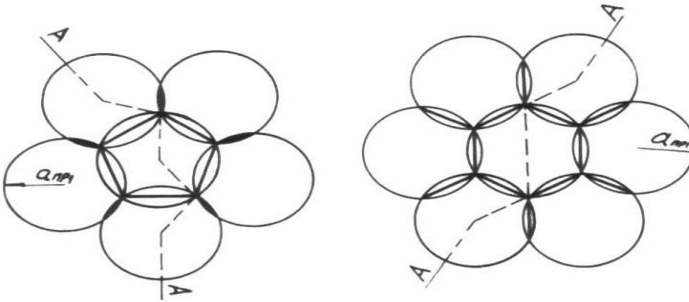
Условная схема расположения пластических отпечатков на обрабатываемой поверхности
